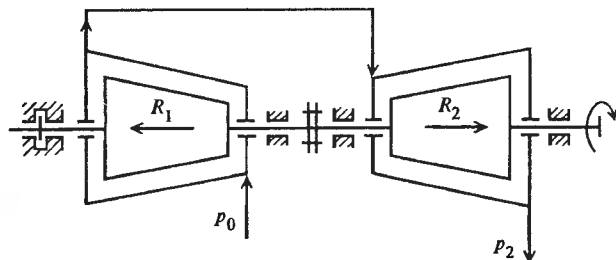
Схема разгрузки упорного подшипника в двухцилиндровой турбине
